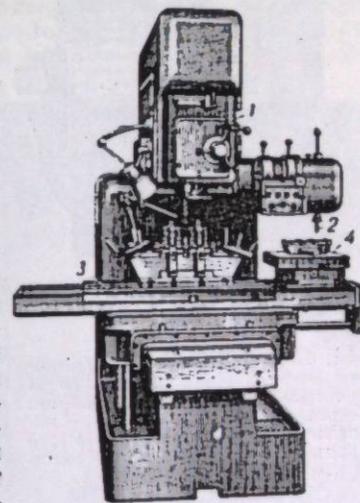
Вертикальный копирующе-фрезерный станок для плоского копирования: 1 — шпиндельная бабка; 2 — копирующая головка; 3 — место крепления изделия; 4 — место крепления копира.
